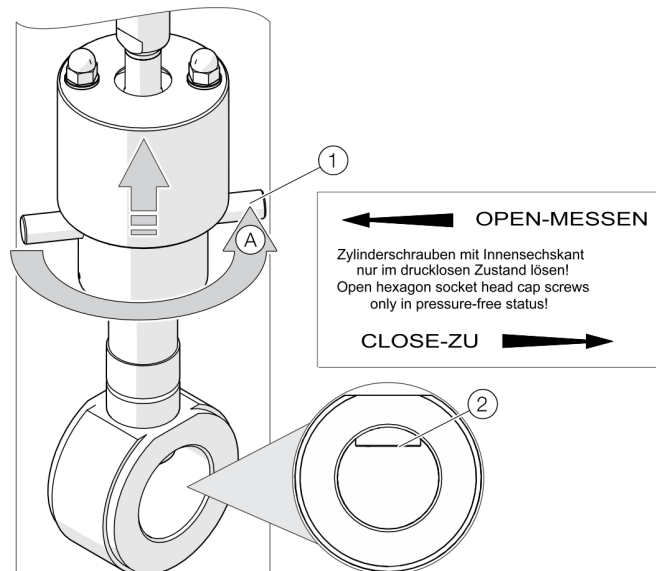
Amener le dispositif de remplacement intégré en position de démontage
